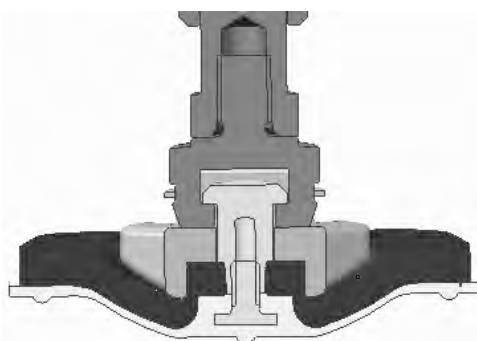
Модульный компрессор с удерживающим кольцом с защелкой для привода Advantage 2.1
